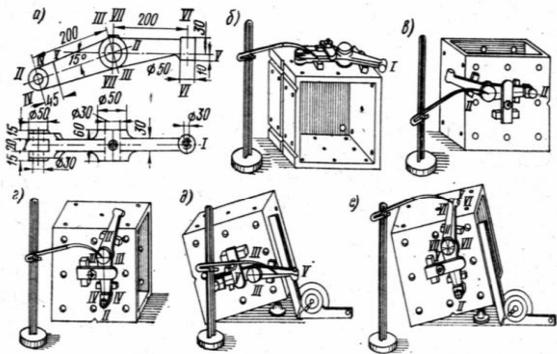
Разметка рычага с помощью установочного приспособления.
